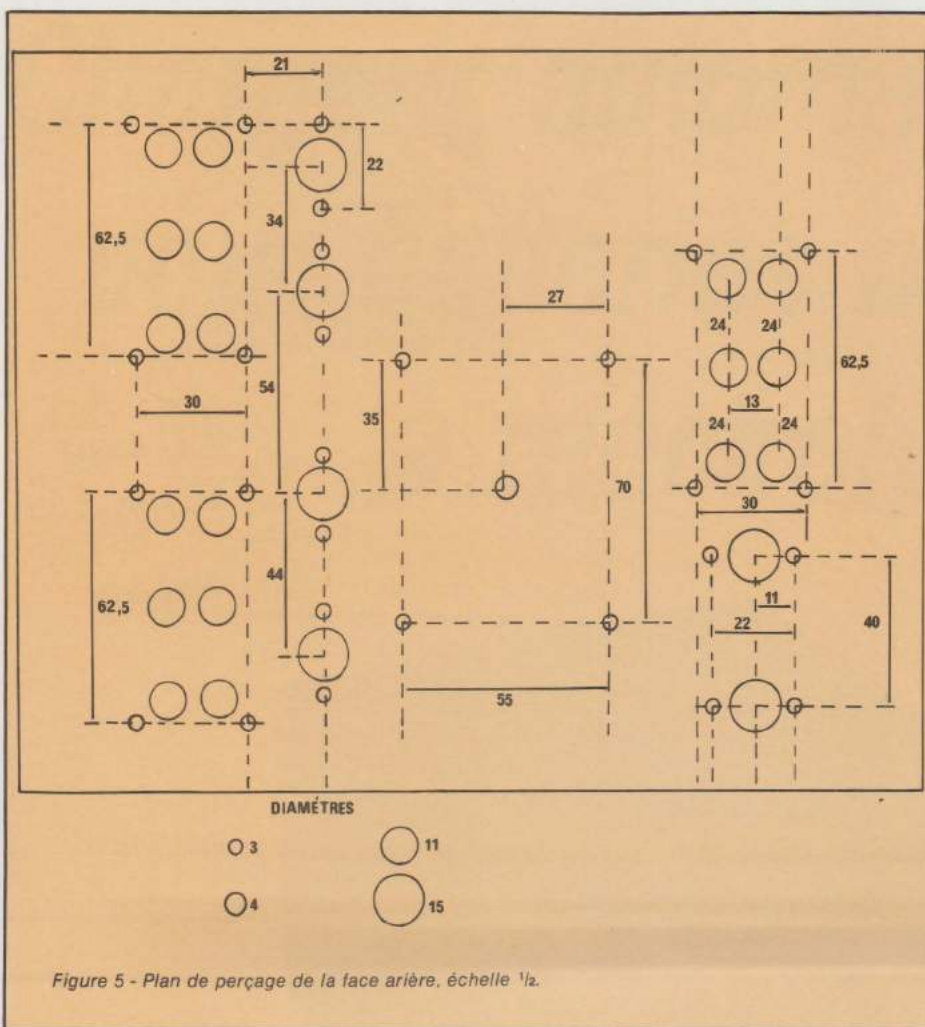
Plan de perçage de la face arrière, échelle 1/2.
